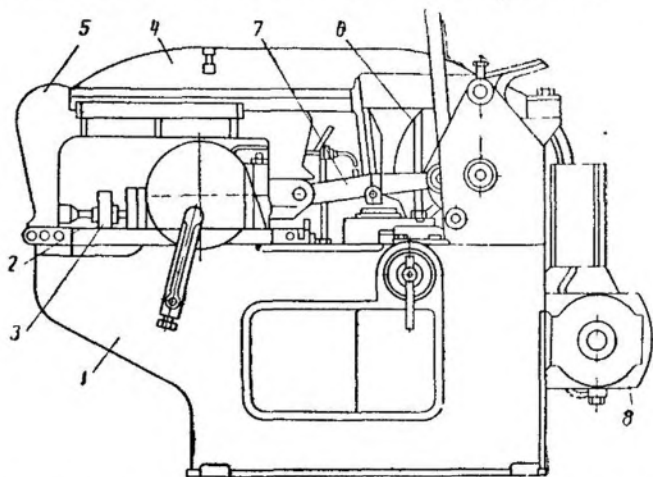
Приводной ножовочный станок 872 Троицкого станкостроительного завода
